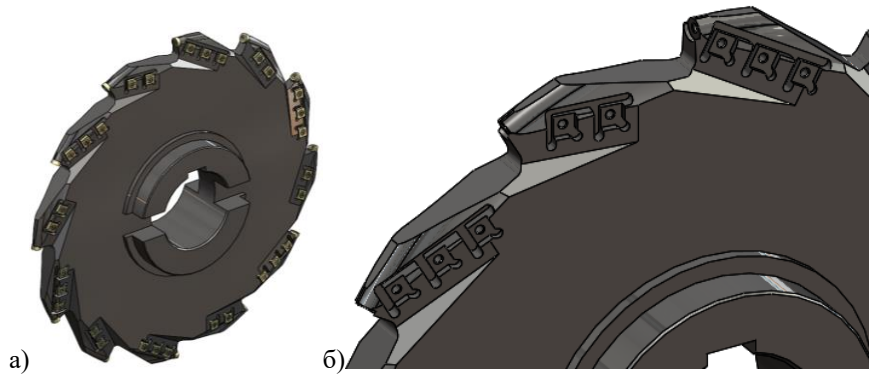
Модель дискової збірної фрези на базі гіперболоїду: а) модель фрези, б) корпус фрези з пазами під НПП
